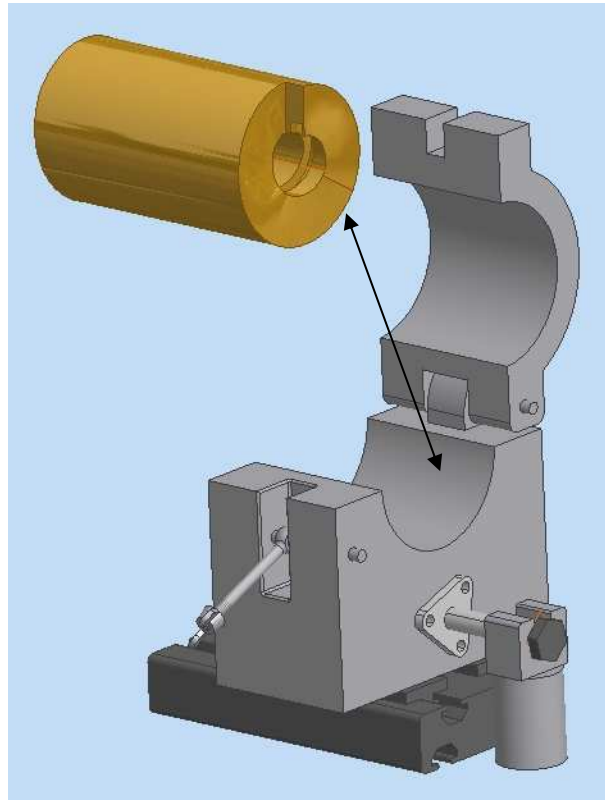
Werkzeugaufnahme beim Schneckenwechsel
